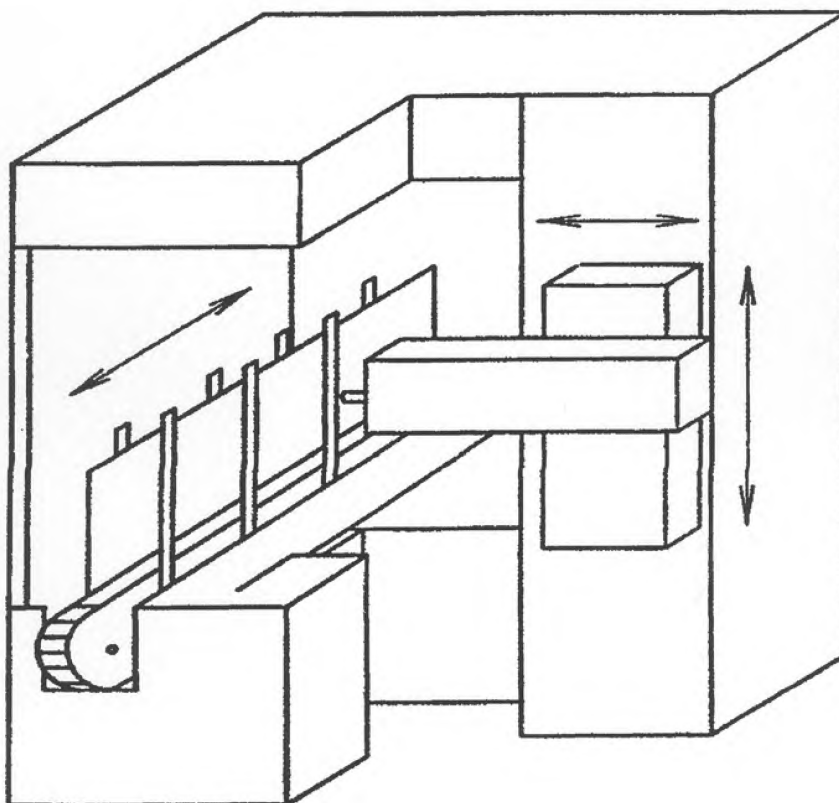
Вертикальный станок (передвижной суппорт, неподвижная рама, подвижная головка)¹
